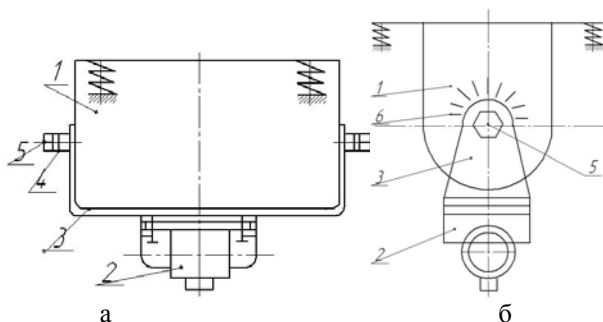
Принципова схема модифікованого вібраційного верстата ВНУ-100: а – загальний вид; б – вид збоку
